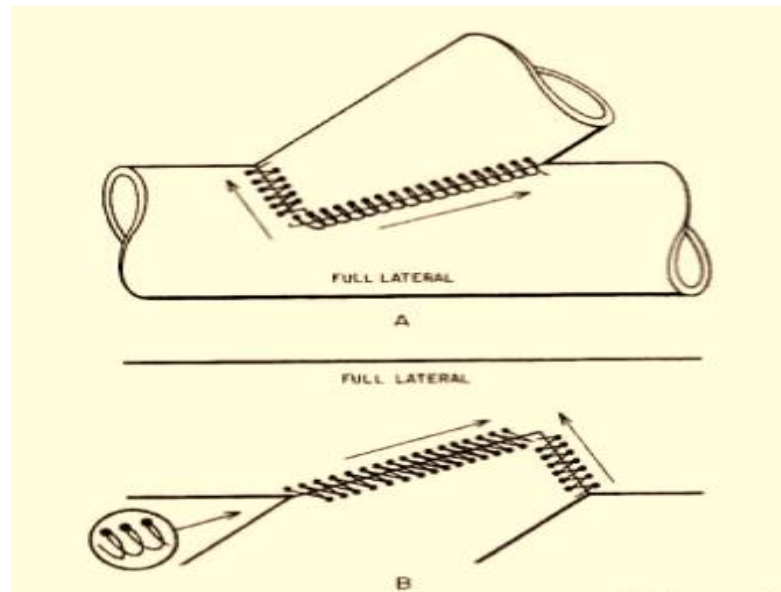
Modèles de tissage utilisés pour souder un joint de conduite latéral. A). Avec la conduite transversale sur le dessus de la conduite horizontale; B). Avec les deux conduites dans une position horizontale. [45]
